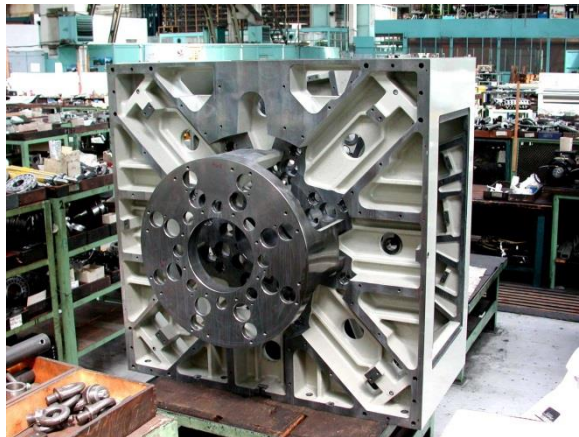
Odlitek základny [TAJMAC-ZPS]Obr. 22 Odlitek základny [TAJMAC-ZPS]
